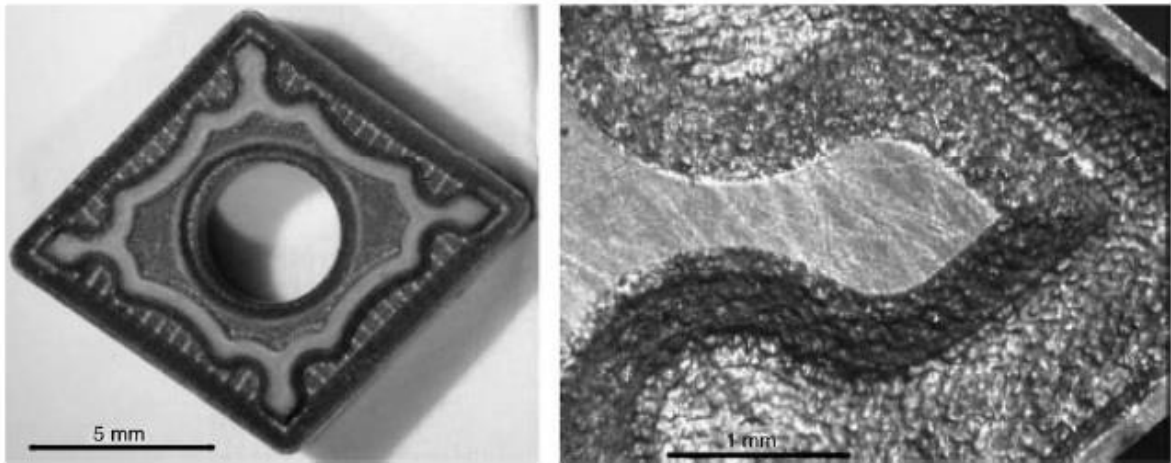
Quebra-cavaco integral fabricado por usinagem a *laser* em ferramenta de corte sinterizada padrão.
